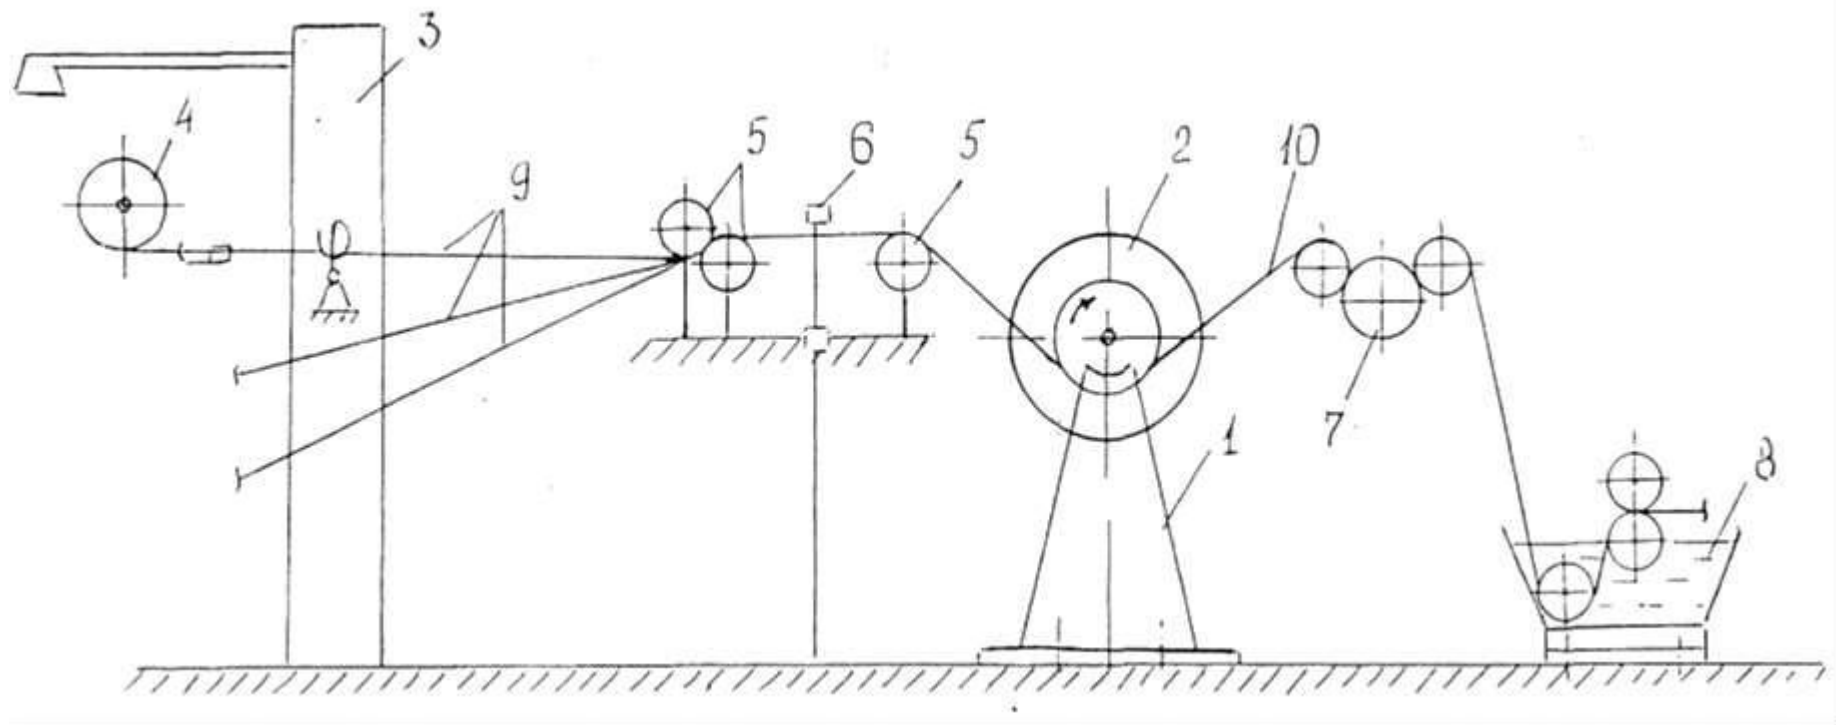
Сновально-шлихтовальный агрегат новой конструкции
